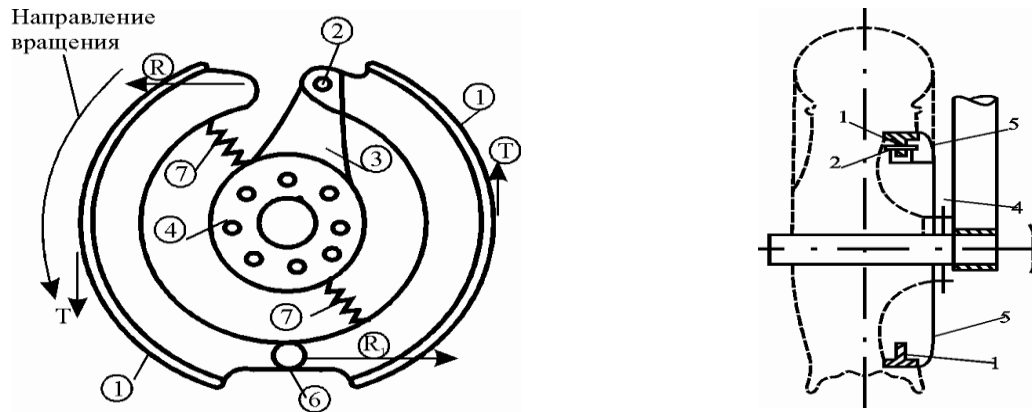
Схема гальма колодки: 1 – колодки; 2 – анкерний болт; 3 – кронштейн; 4 – фланець; 5 – чашка; 6 – шарнір; 7 – пружини
